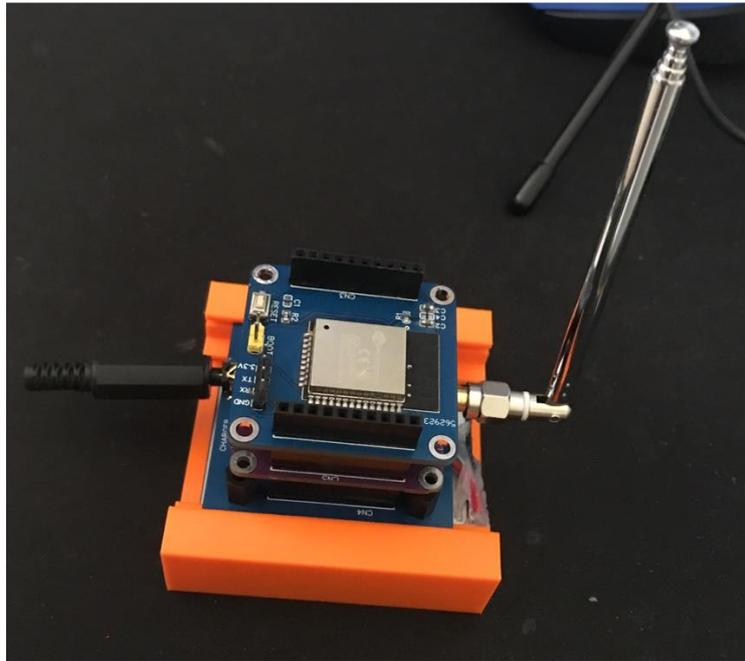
PCB e Componentes do Segmento de Voo Versão 4.0.
